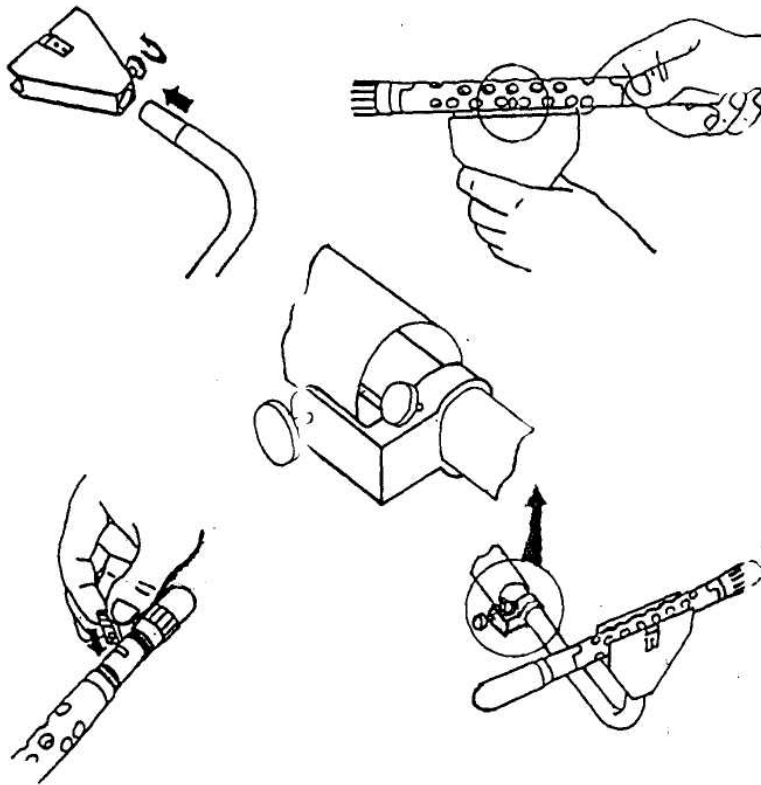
Порядок сборки и установки пробозаборника
